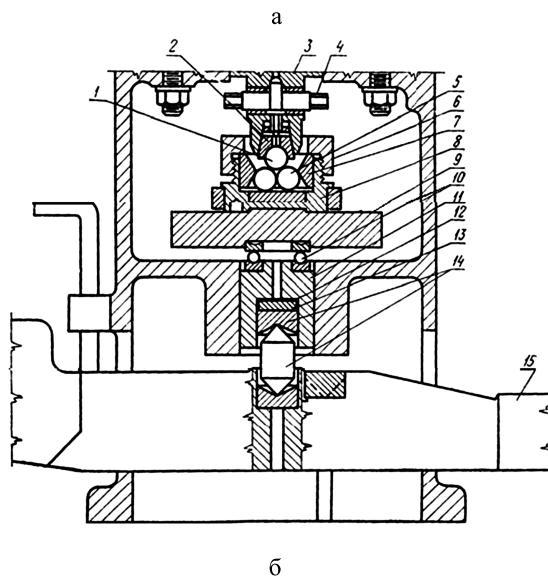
Чотирикулькова машина тертя (а) та її робочий вузол тертя (б): 1 – верхня кулька; 2 – патрон; 3 – шпиндель; 4 – шпилька; 5 – три нижні кульки; 6 – гайка; 7 – шайба; 8 – чашка; 9 – диск; 10 – упорний підшипник; 11 – втулка; 12 – бронзова прокладка; 13 – резинова прокладка; 14 – ножова опора; 15 – важіль перемінних ваг.
